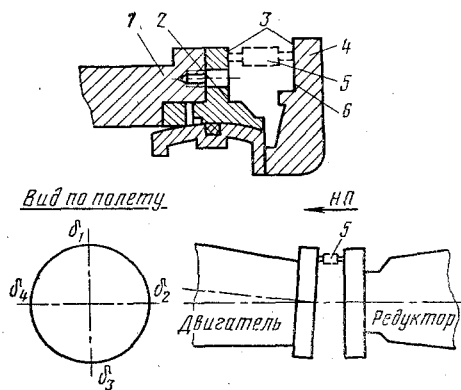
Схема замера несоосности двигателя с главным редуктором при установке на вертолет:
